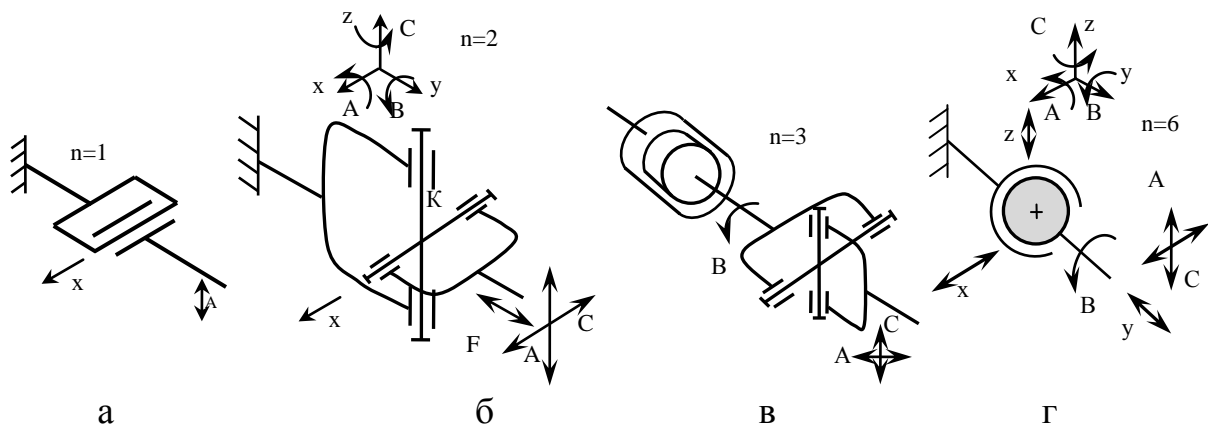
Кінематичні схеми шарнірів систем приводів: а – однокоординатний шарнір; б – двохкоординатний (карданний) шарнір; в – еквівалентна схема трьохкоординатного (сферичного) шарніра; г – регульований шестикоординатний сферичний шарнір в якому реалізовані мікропереміщення сфери в просторі
